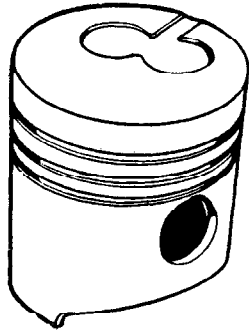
Pistón de un motor pequeño con inyección indirecta
